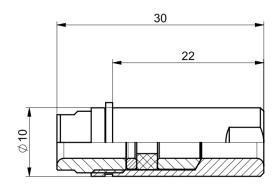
Adapter Typ 1700A37B (für Kabel ohne Kabelschutz)
